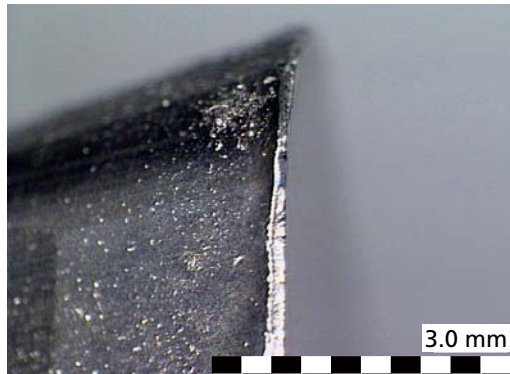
Werkzeug-Verschleiß als Grenze beim Fräsen von Tellerrädern
